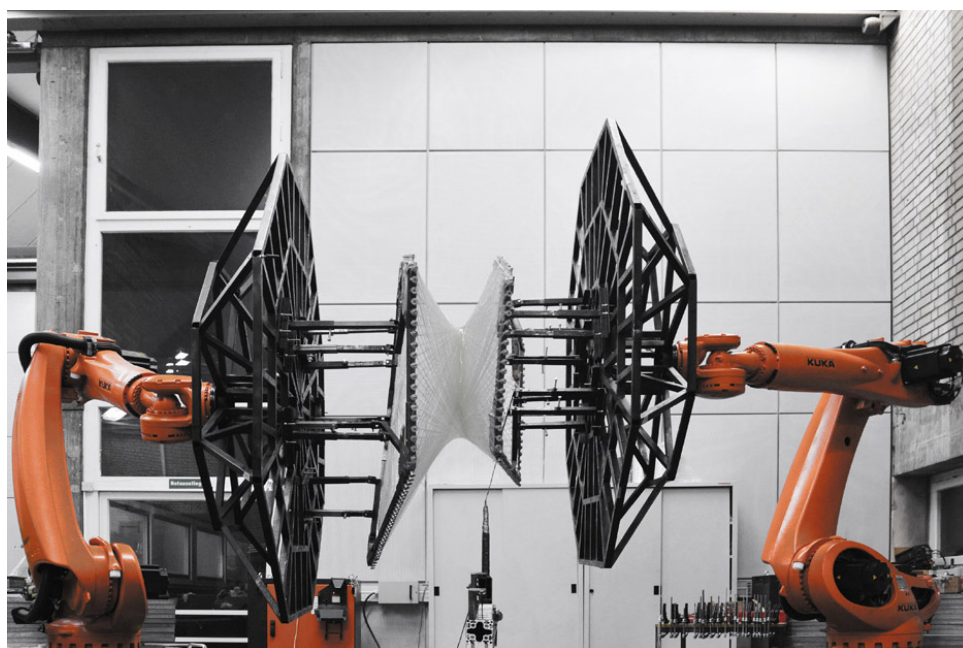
Par de robôes KUKA construindo protótipo para o V & A pavilhão
